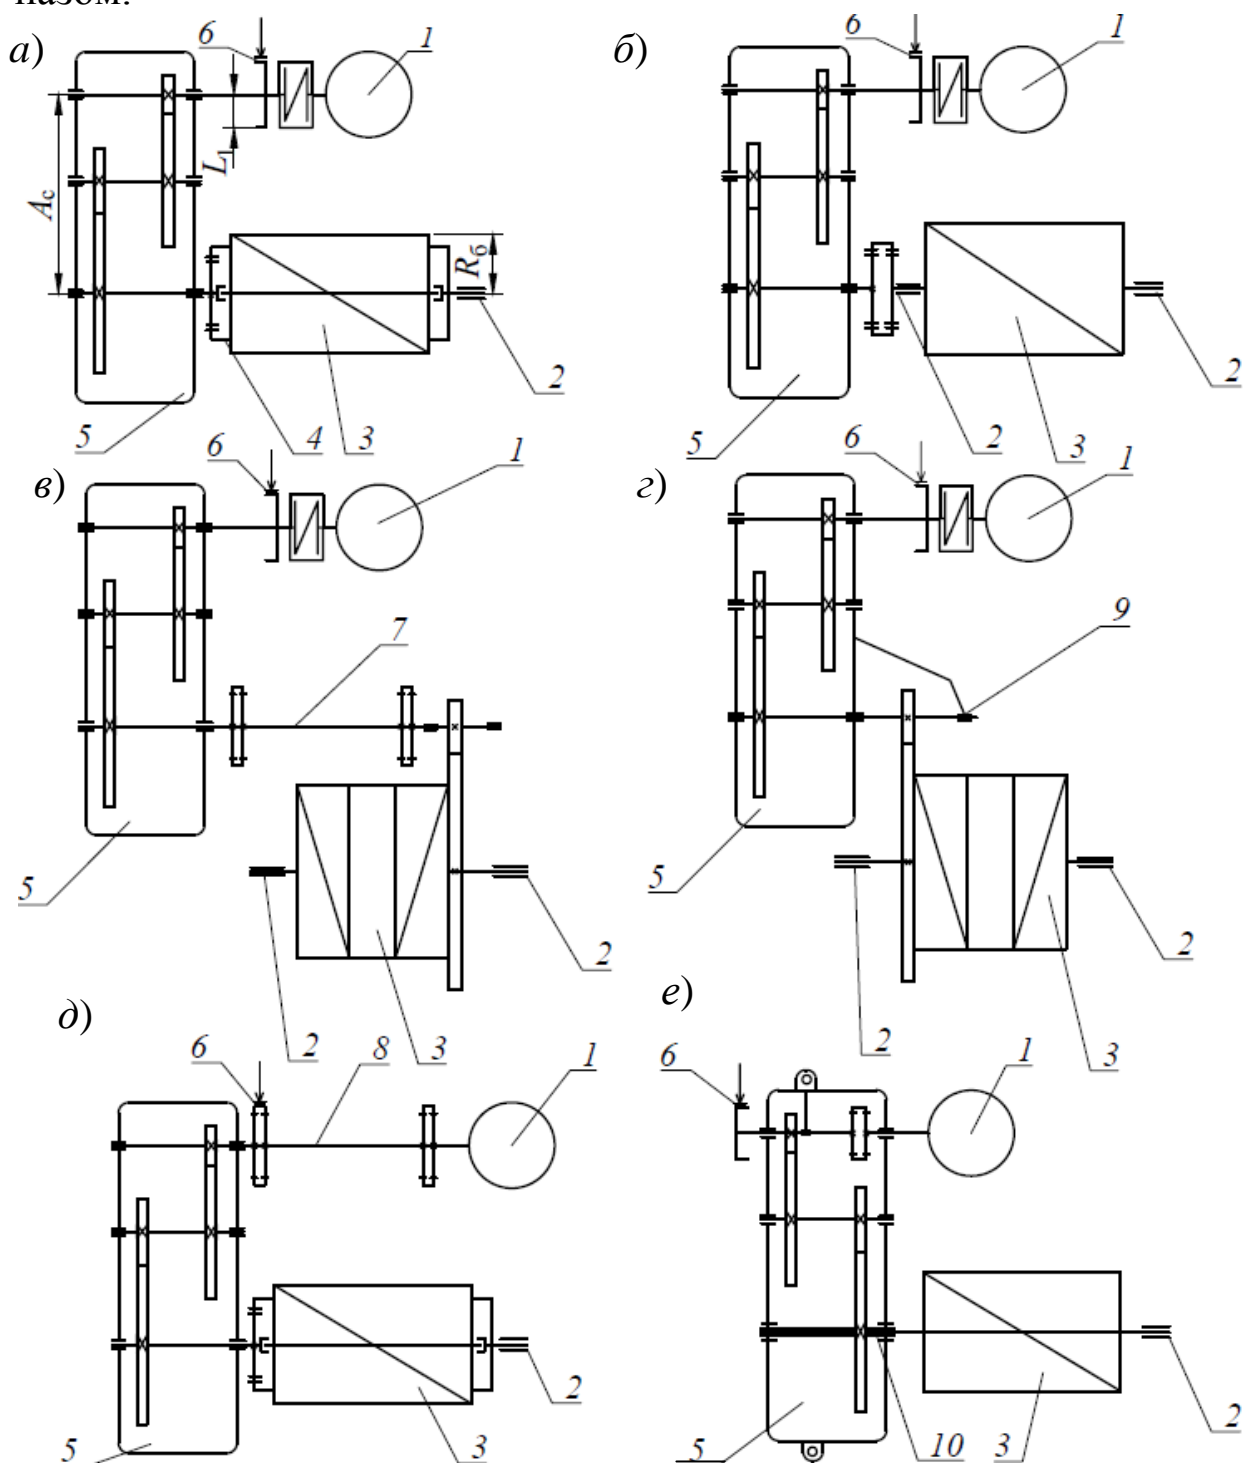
Компонировочные схемы механизма подъема: *а* – со встроенной в барабан зубчатой муфтой; *б* – с дополнительной муфтой; *в* – с тихоходным валом-вставкой; *г* – с открытой зубчатой передачей; *д* – с быстроходным валом-вставкой; *е* – с полным тихоходным валом редуктора
